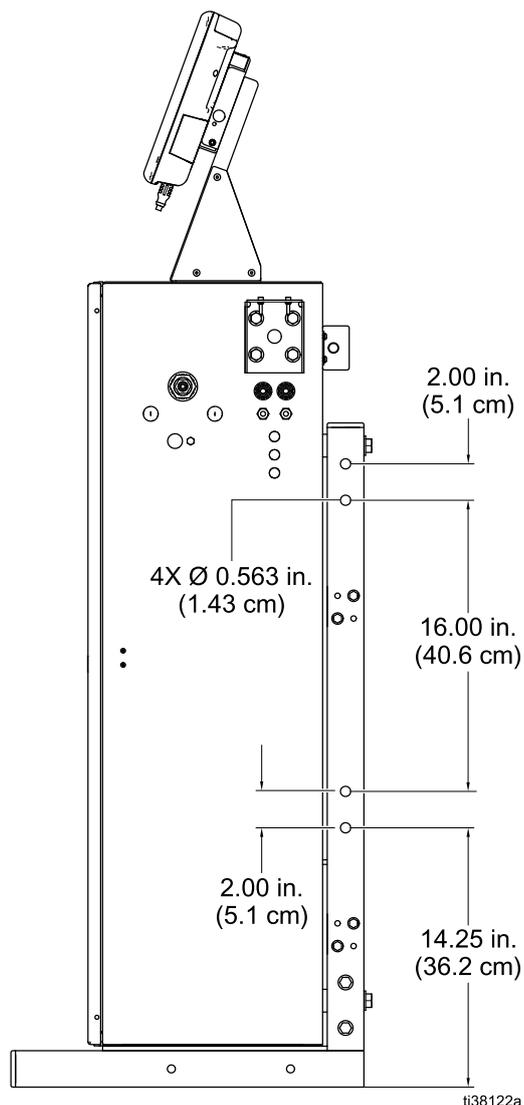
Схема расположения монтажных отверстий для настенного монтажа
